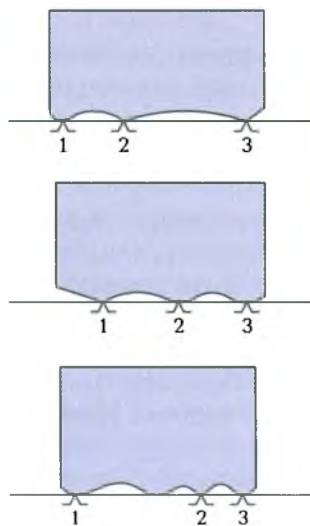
Различные схемы установки деталей необработанной поверхностью на плоскую поверхность стола станка
